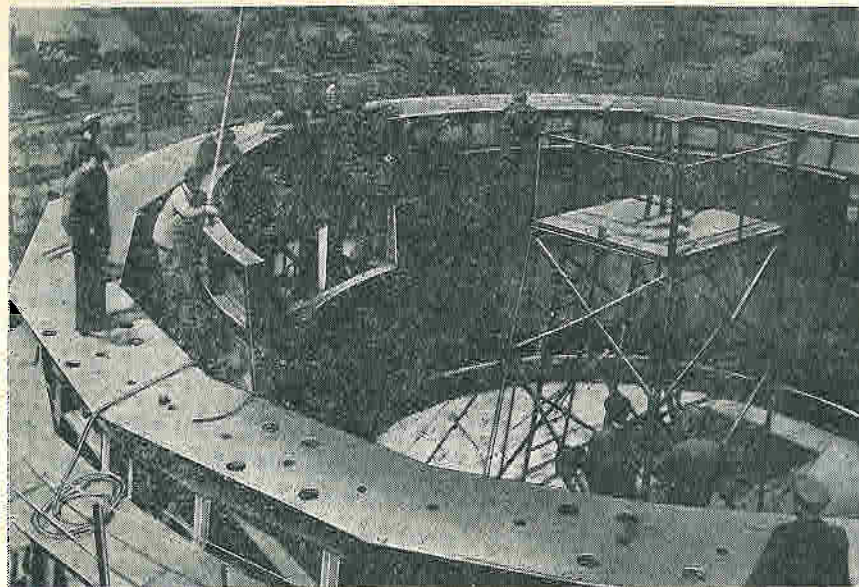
Установка сегментов камеры рабочего колеса поворотно-лопастной гидротурбины
